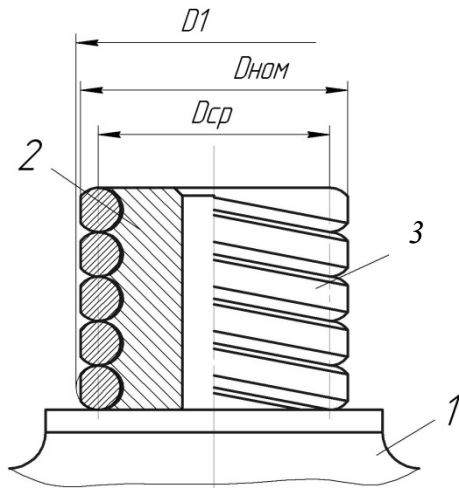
Карданный шарнир с витой цилиндрической пружиной из проволоки круглого сечения
